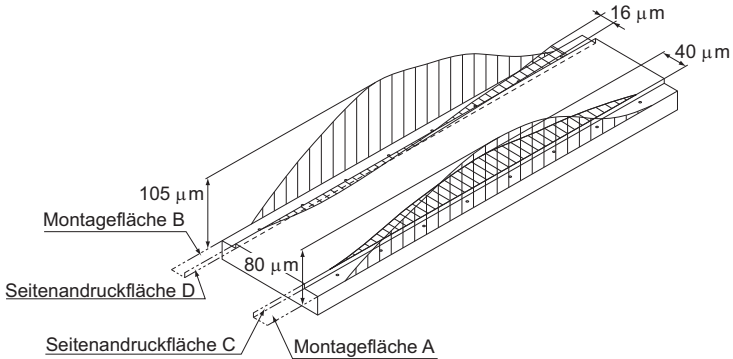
Oberflächengenauigkeit der Montagefläche der Linearführung (nur gefräste Oberfläche)
